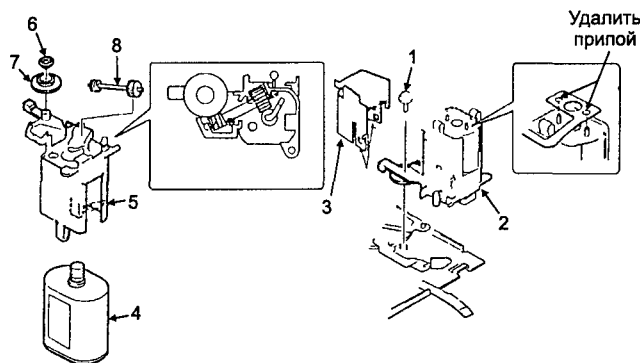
Узлы системы заправки кассеты и ленты видеокамер Sony с механизмом В. Условные обозначения: 1 — M1,4x2,5, 2 — узел блока держателя двигателя, 3 — экран двигателя, 4 — узел двигателя, 5 — муфта держателя двигателя, 6 — держатель двигателя, 7 — шестерня А, 8 — червячный вал.
